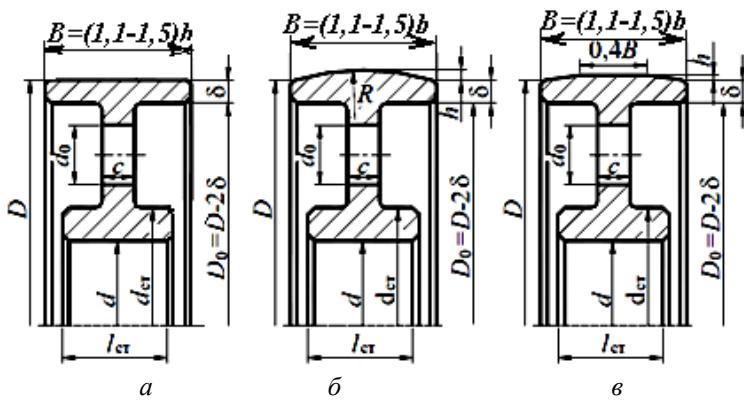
Варіанти конструкцій шківів (b - ширина паса)
